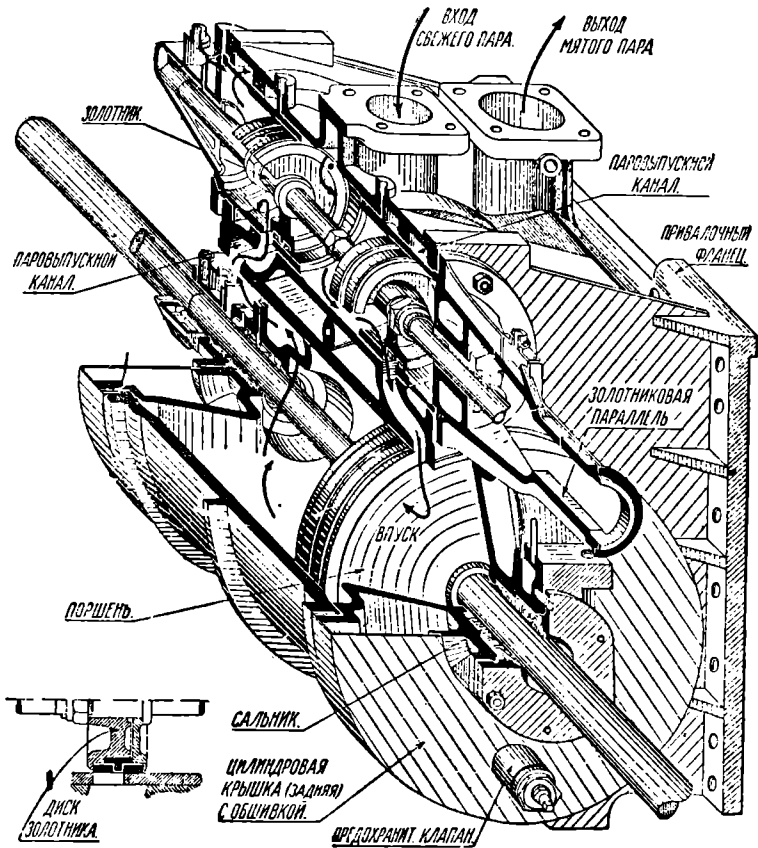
Поршень и цилиндрический золотник паровоза серии Эу.
